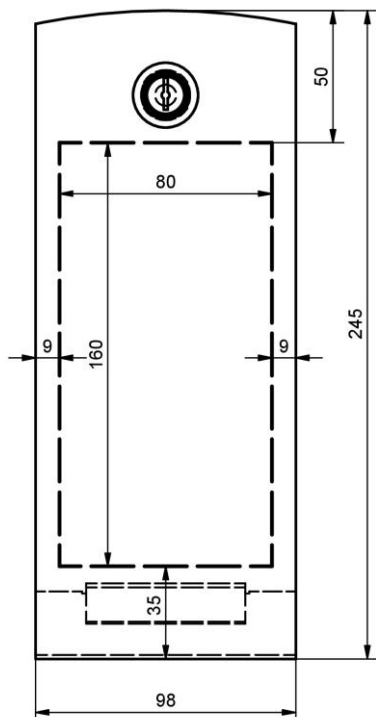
Einbaubereich (160mm x 80mm) für Einbauten in die Frontplatte
